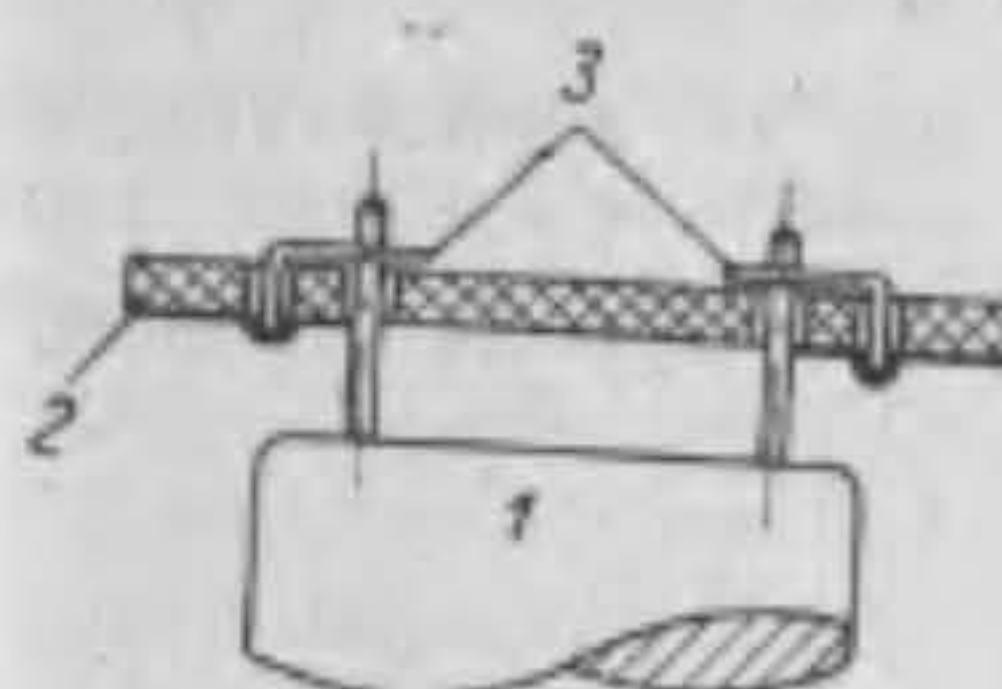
Montarea unui tub electronic direct pe placă prin fixare în contacte în V;
